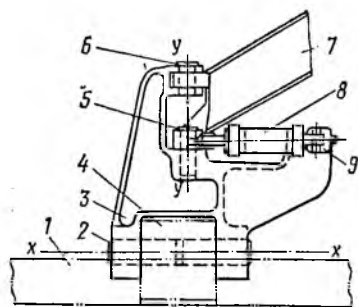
Поворотнo-сцепное устройство скрепера ДЗ-11:
